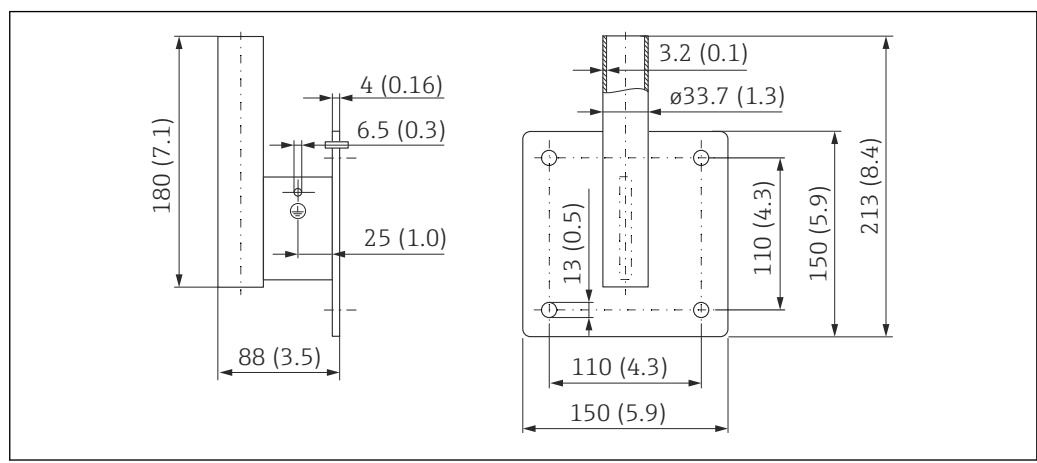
Dimensiones del soporte para montaje en pared. Unidad de medida mm (in)
